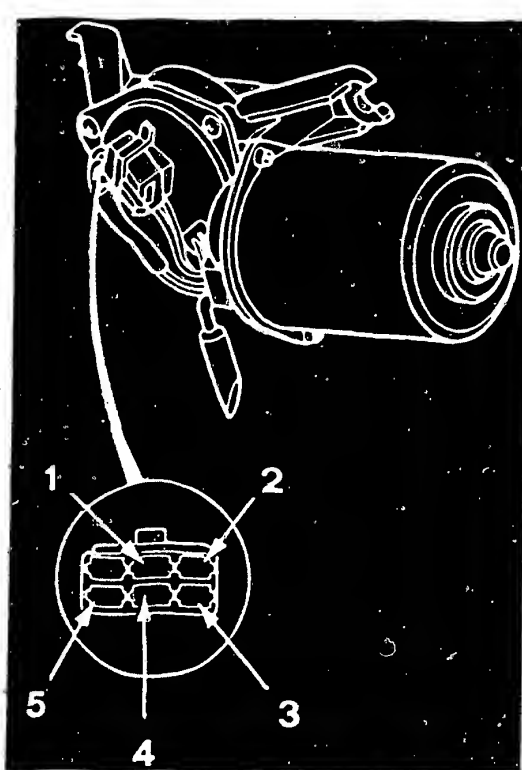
Wischermotor mit Steckanschluss. Prüfwerte siehe Text.
